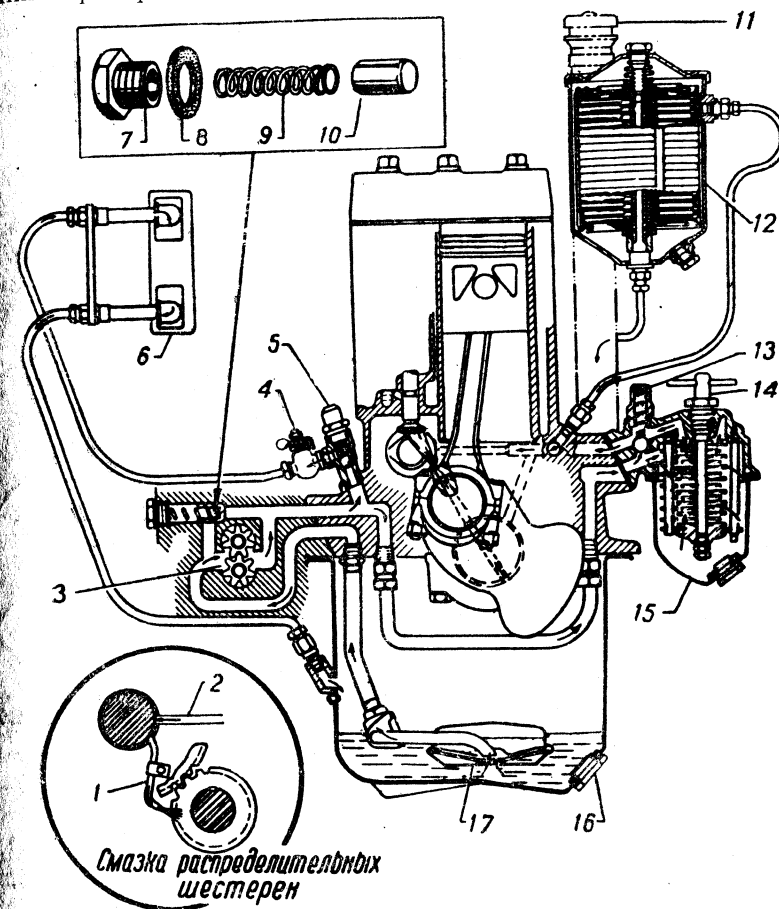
Схема смазки двигателя без центробежного фильтра. 1—ключ, 2—масляный канал к подшипникам коленчатого и распределительного валов, 3—шестерни масляного насоса, 4—кран масляного радиатора, 5—предохранительный клапан, 6—масляный радиатор, 7—пробка, 8—прокладка, 9—пружина, 10—плунжер, 11—крышка масляного патрубку, 12—фильтр тонкой очистки, 13—перепускной клапан, 14—фильтр грубой очистки, 15—фильтр грубой очистки, 16—сливная пробка, 17—маслоприемник.
